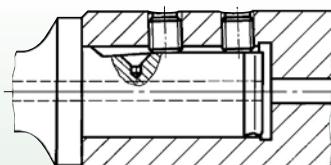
Хвостовик сверла по DIN 6595/ISO 9766 и крепление с помощью двух винтов с плоским торцем.
